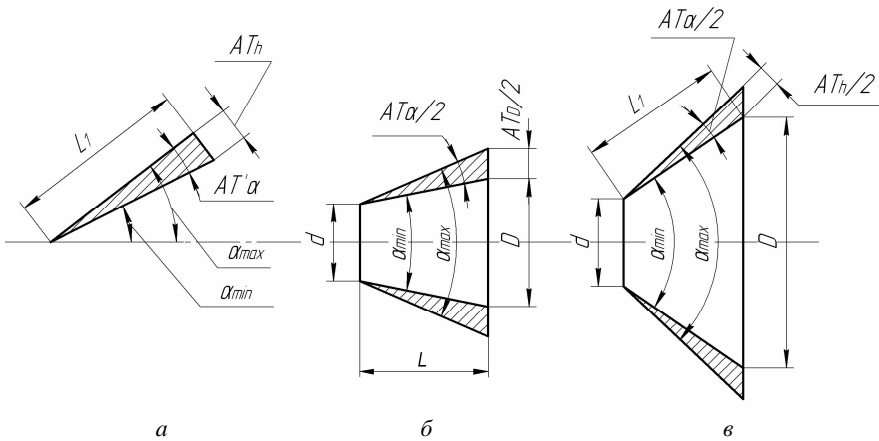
Расположения полей допусков углов и конусов:
